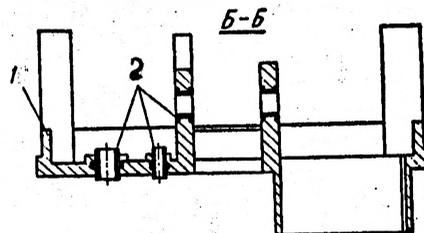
Корпус механизма. 1 – тело отливки, 2 – арматура.
